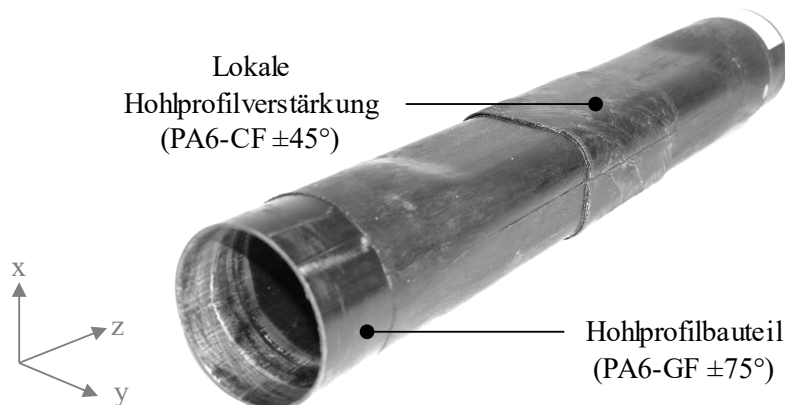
Hohlprofilbauteil WZ 09.7 mit lokaler Hohlprofilverstärkung
